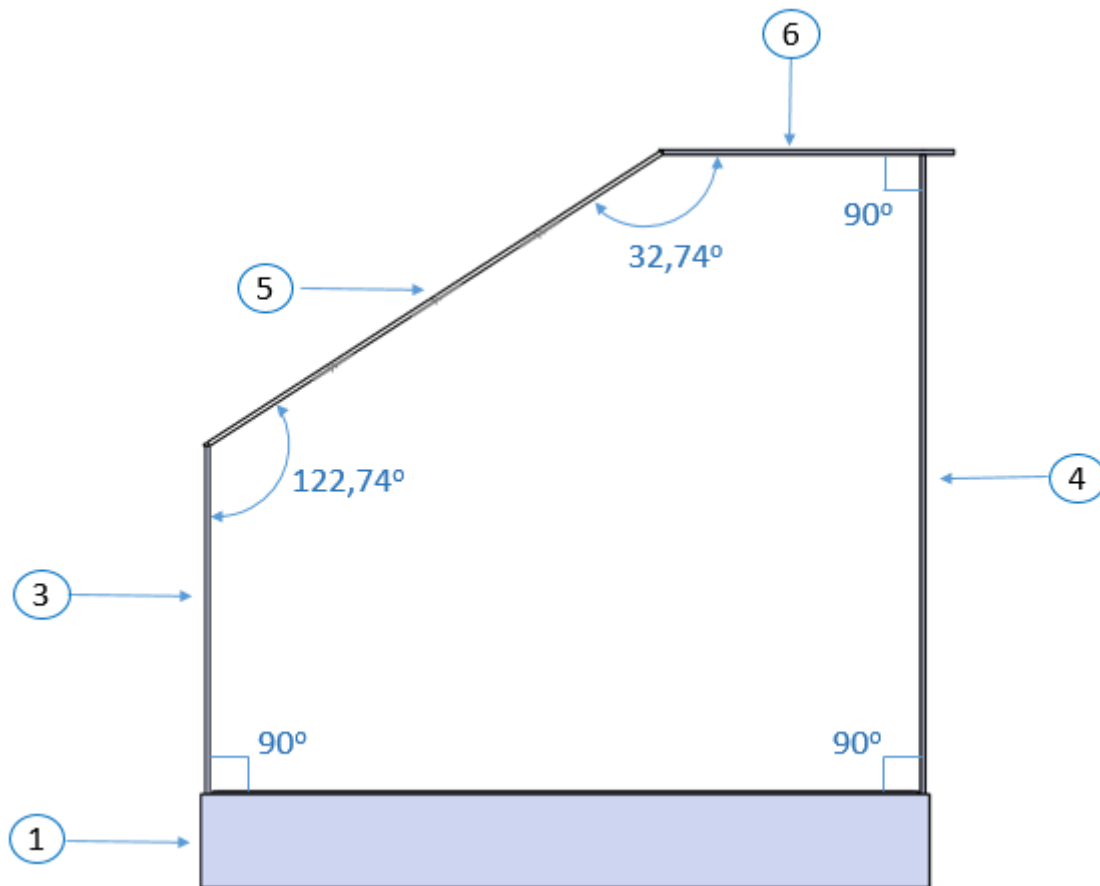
Imagem lateral da Caixa com os respectivos ângulos entre os componentes [Tampa (1); Base (2); Suporte Frontal (3), Suportes Traseiros (4), Superfície Inclinada (5) e Superfície Superior (6)].
